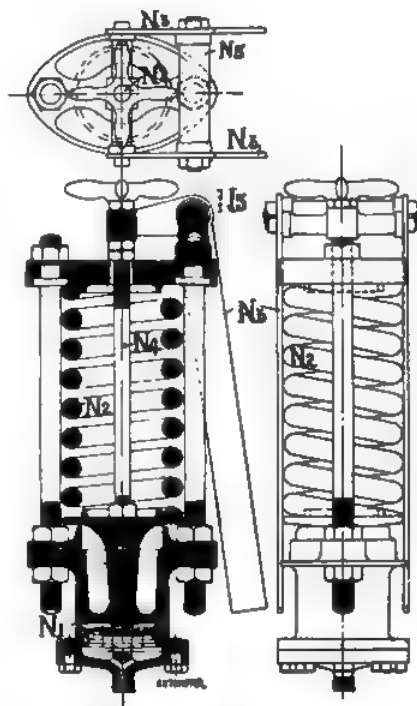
Schnitt durch Excenterpumpe, rechts: Ansicht; oben: Grundriss.
